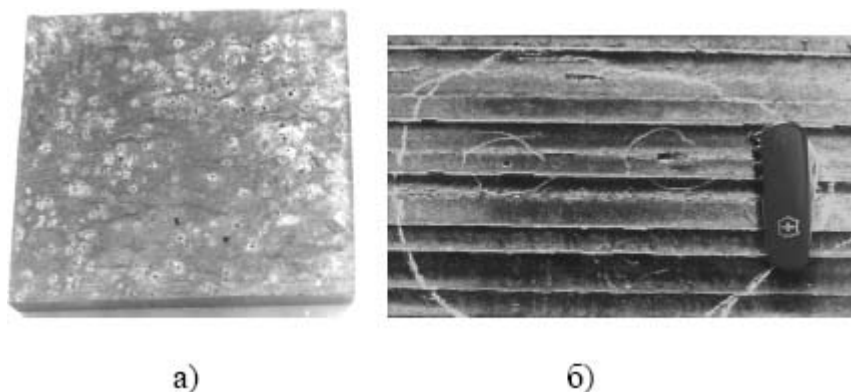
Пузыри и поры на поверхности непрерывнолитой сортовой заготовки (а) и блюма (б)
